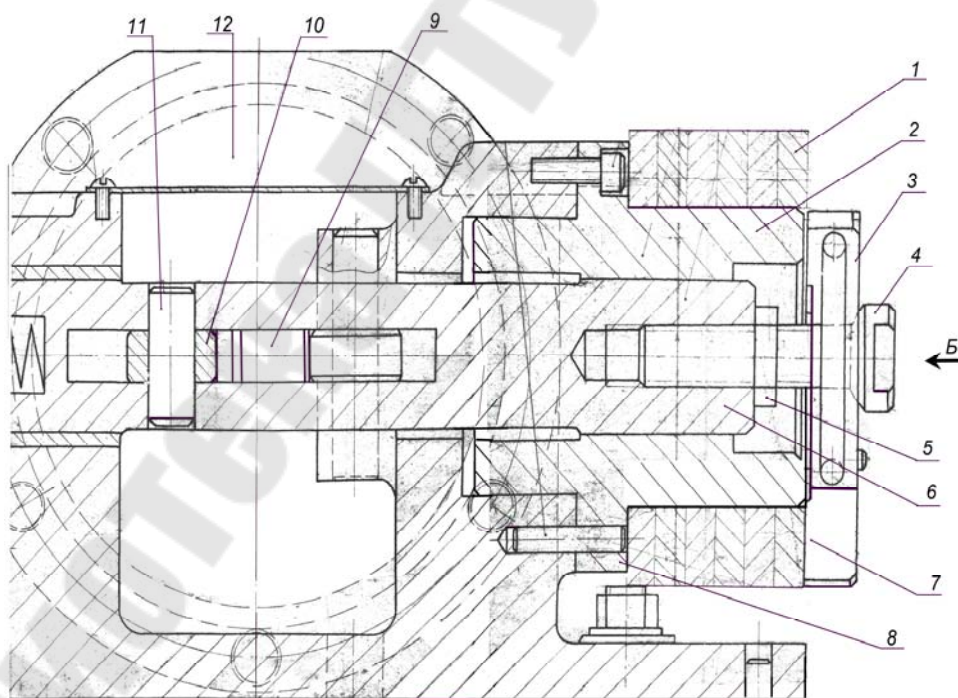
Приспособление для горизонтально-фрезерной операции фрезерования двух уступов
